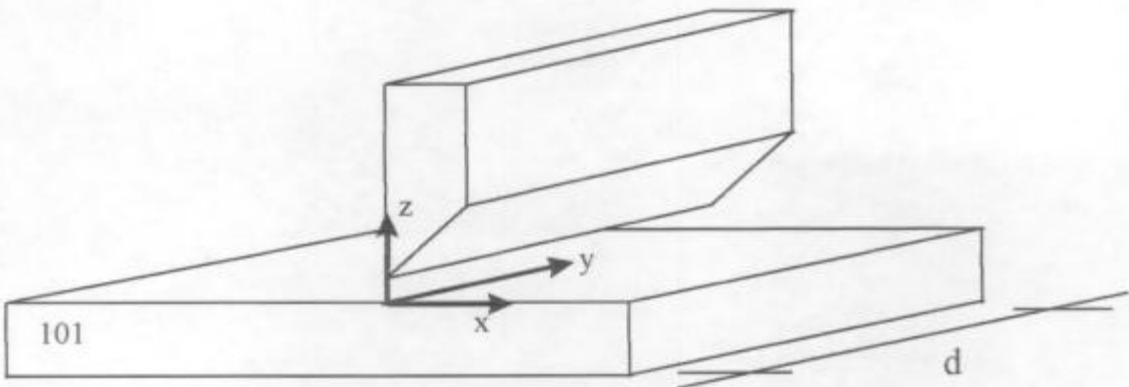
Identificación de las probetas y longitud del cordón de soldadura d.
